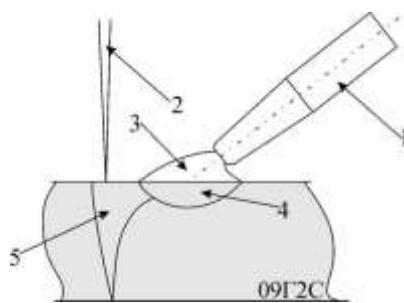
Схема процесса гибридной лазерной сварки
